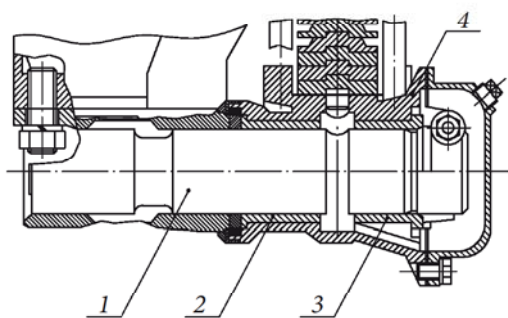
Схема установки подшипников скольжения в балансирной подвеске: 1 — оси; 2 и 3 — подшипники скольжения; 4 — балансирное устройство
